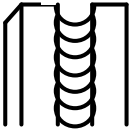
Influencia de la ranura del rodillo en el alambre de soldadura
